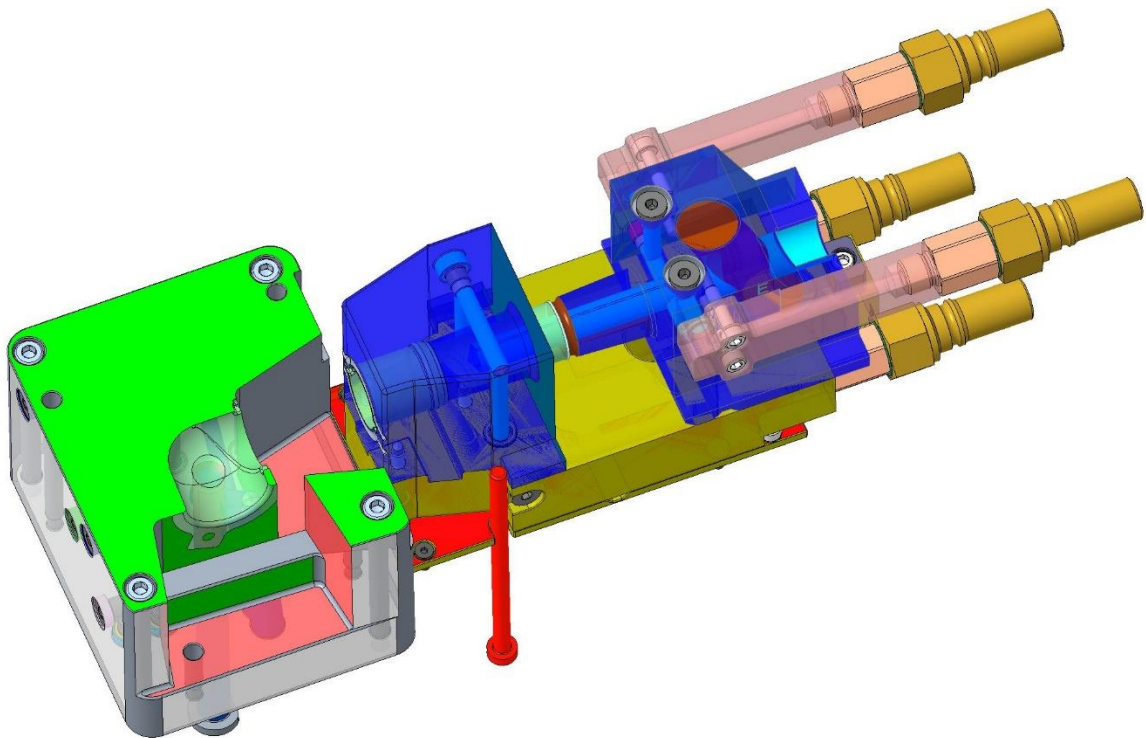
Vyhazovač s odvzdušňovací drážkou (hnědá) a s tvarovou částí, jež je součástí tvarové dutiny formy (světle zelená)
